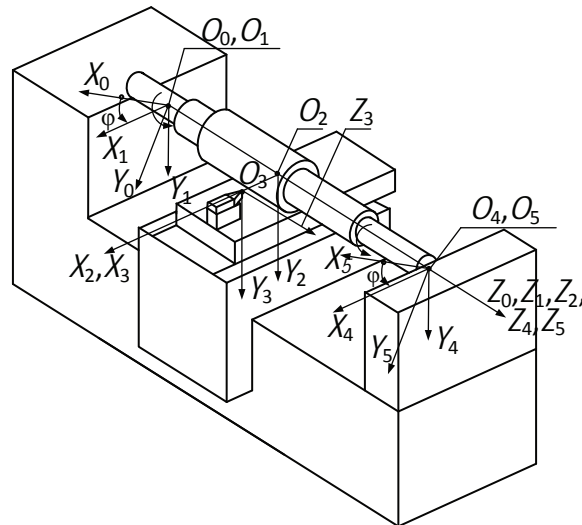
ФС токарного станка с дополнительным замкнутым контуром
